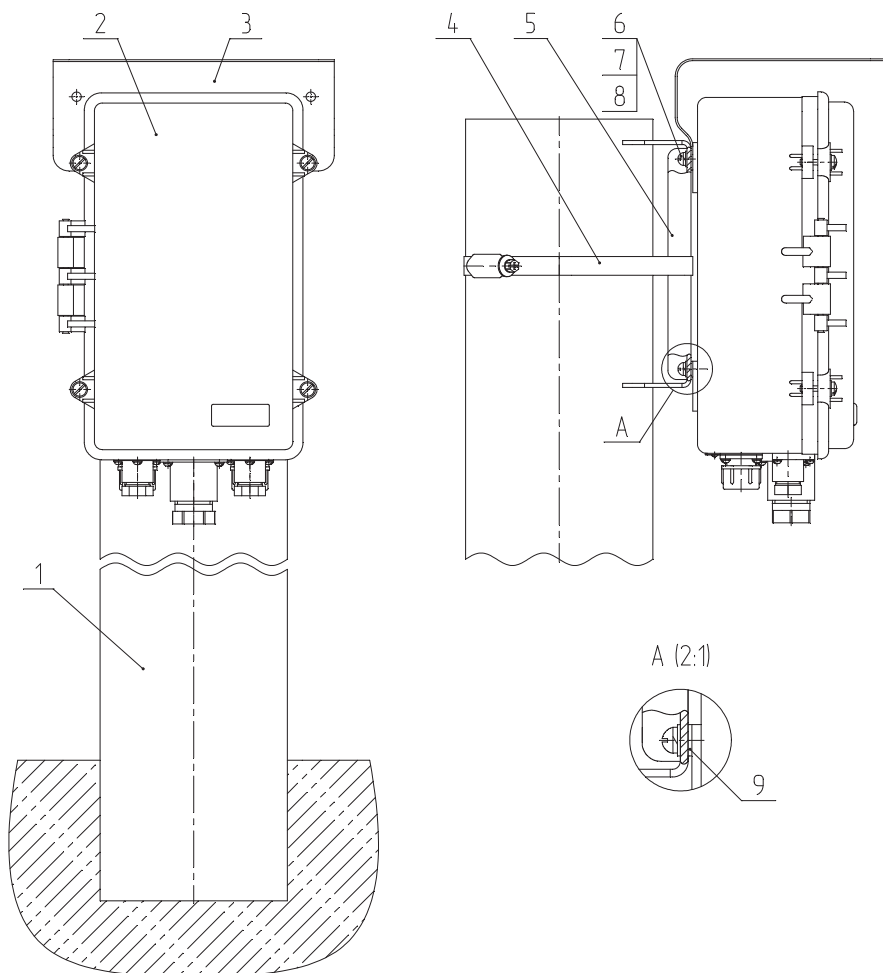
Крепление БЗ на ограждении из железобетонных плит или кирпичной стене
